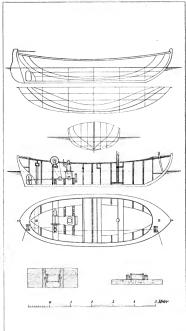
Borfchiag ju einem fleineren beutiden Offeefutter mit Petroleummotor und Gulfsichraube. Gegelzeichnung.
